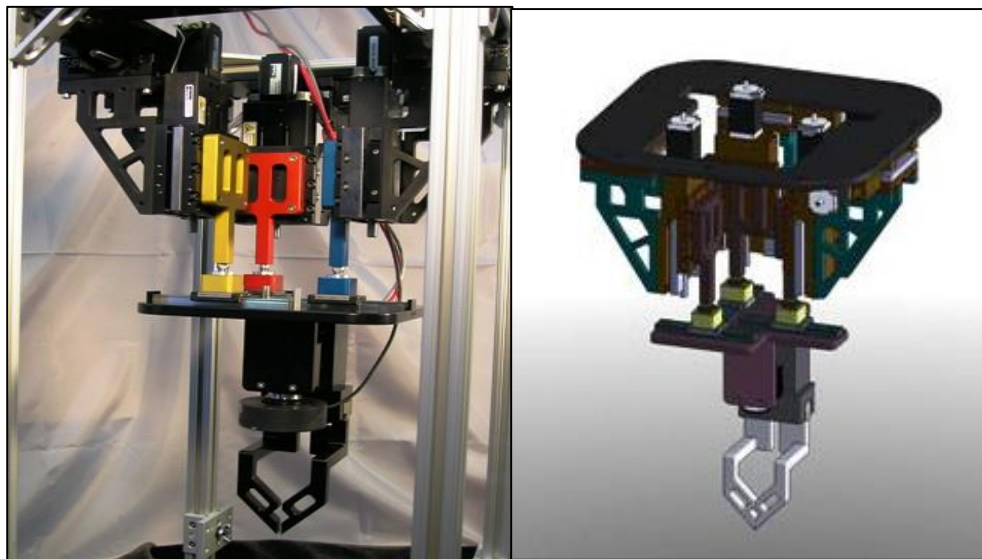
Ensamble en SolidWorks y Manipulador CARMA fabricado.
